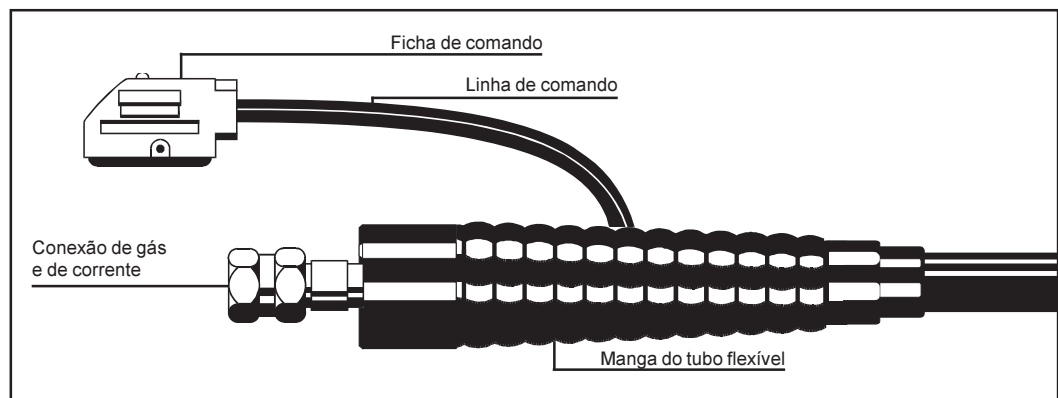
Modelo com ligação central do queimador GWZ: Ligação do queimador refrigerado a gás
